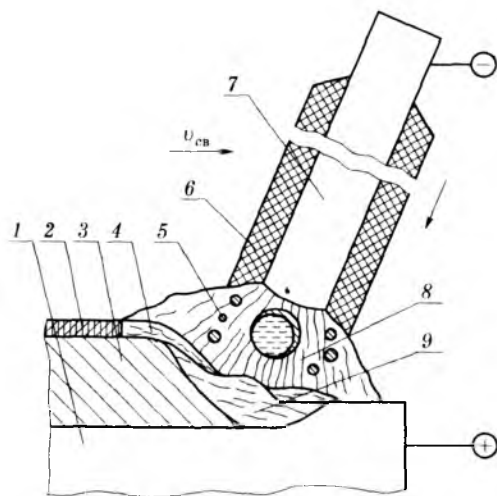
Схема электрической дуги ($v_{св}$ — направление сварки):
